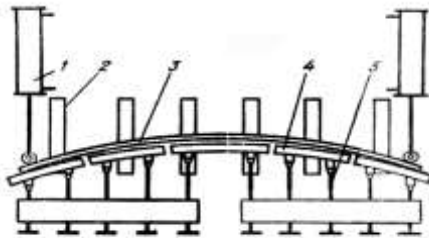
Схема машини для згинання рейок після загартування: 1 - пневматичний нажимний пристрій; 2 - рольганг; 3 - рейка; 4 - упор; 5 - гвинти для зміни радіуса упору [9]
